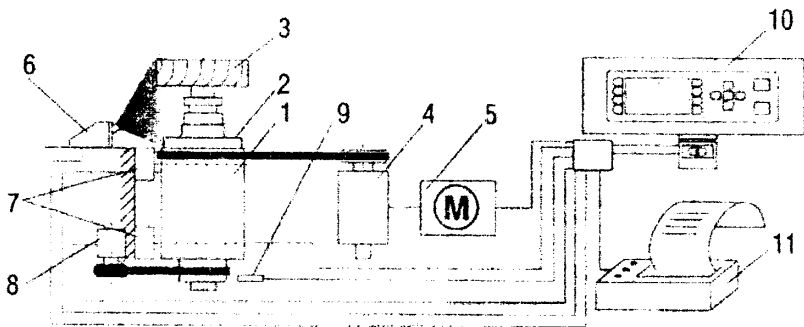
Схема работы вертикальной балансировочной машины Profi Tool Balancer фирмы Hofmann Mess- und Auswuchttechnik
